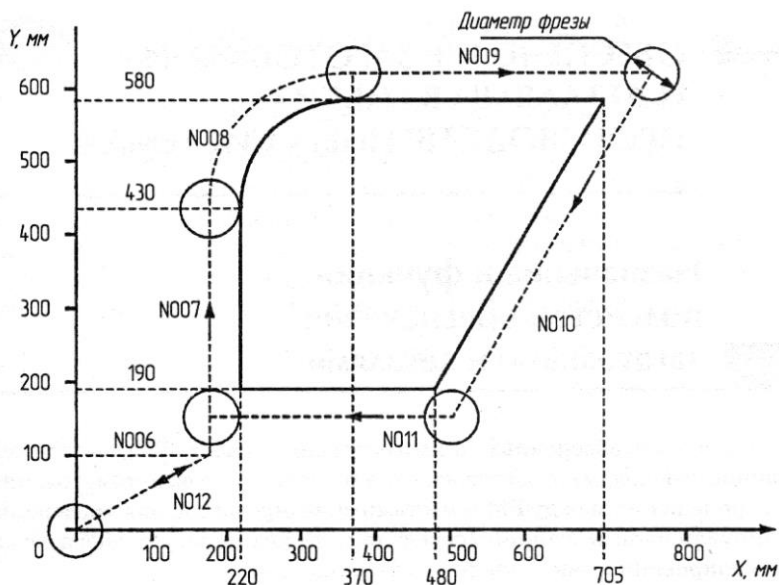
Движение фрезы по эквидистанте при фрезеровании
